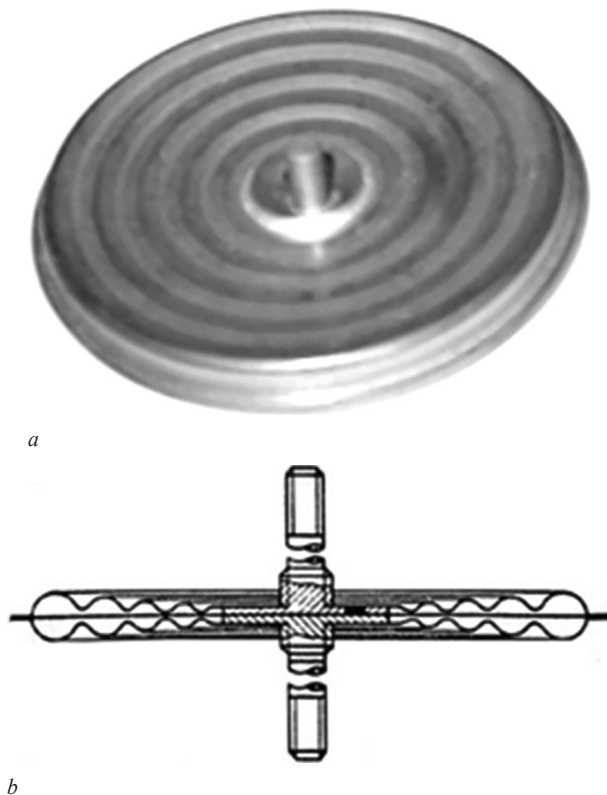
Внешний вид (a) и схематическое изображение (b) конструкции АЧЭ-286
